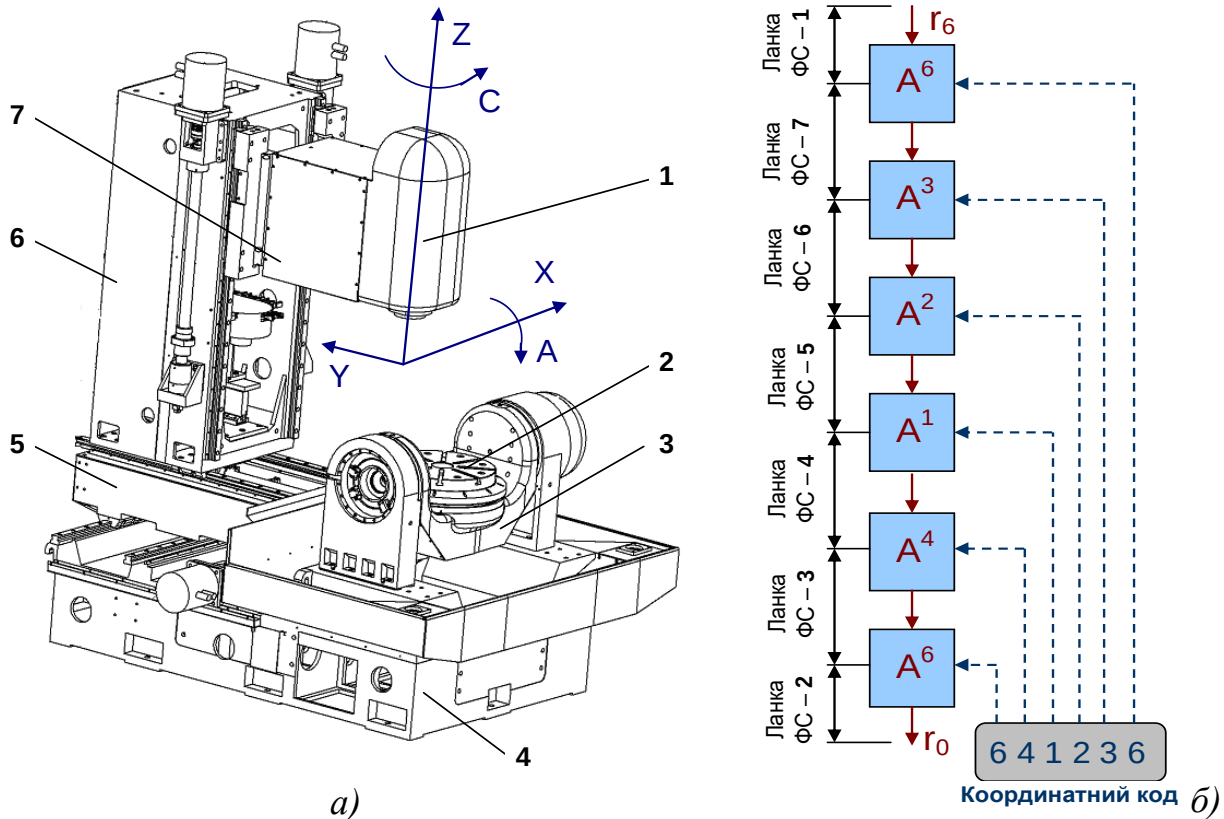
Основні вузли (а) та формуюча структура п'ятикоординатного багатоцільового верстата з ЧПК: 1 – шпиндель; 2 – вертикальний поворотний стіл; 3 – горизонтальний поворотний стіл; 4 – основа; 5 – поперечний стіл; 6 – рухома стійка; 7 – шпиндельна бабка
